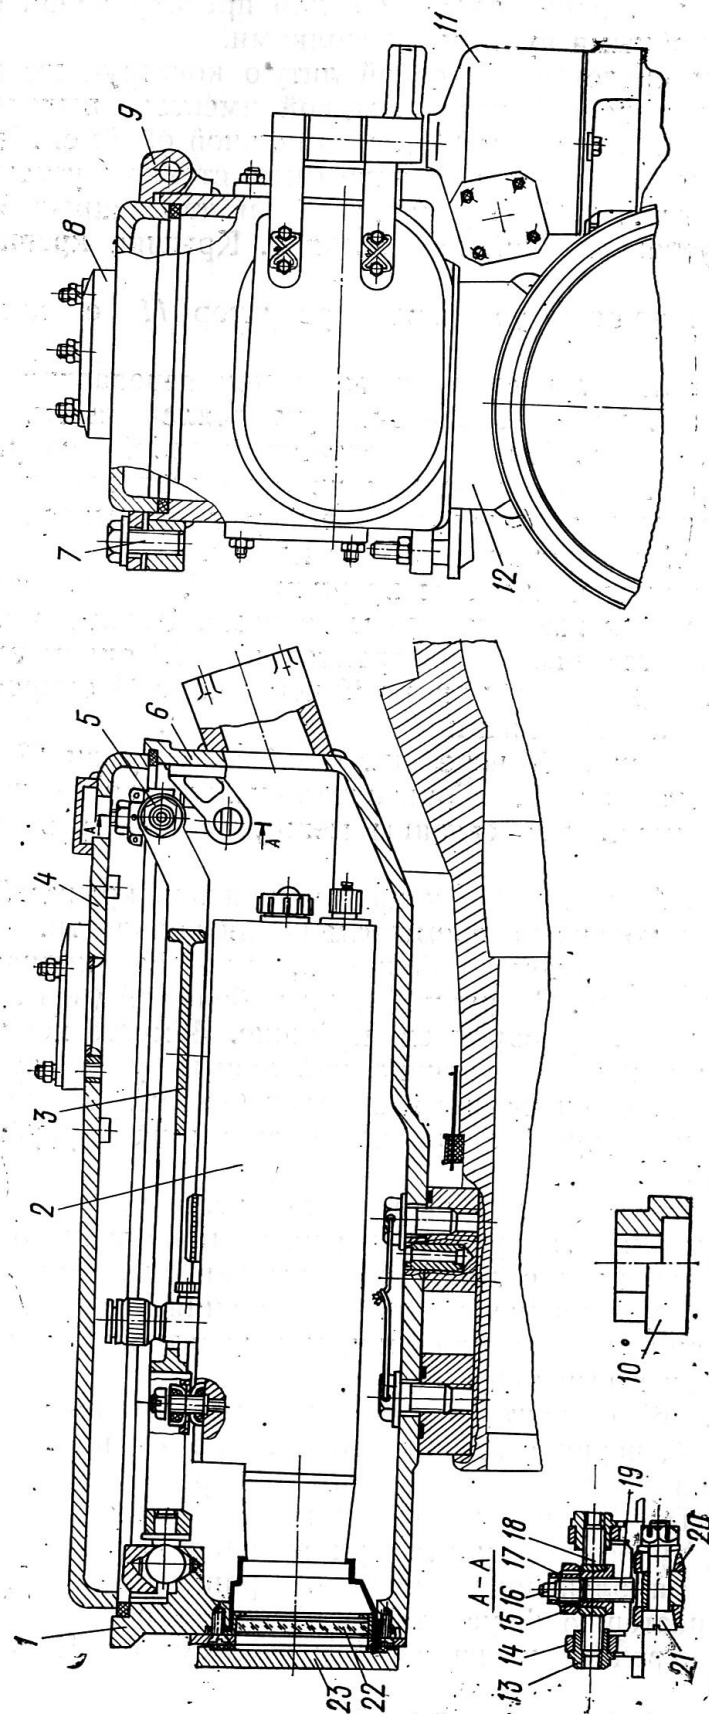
Установка приемопередатчика дальномера КДТ-2:
